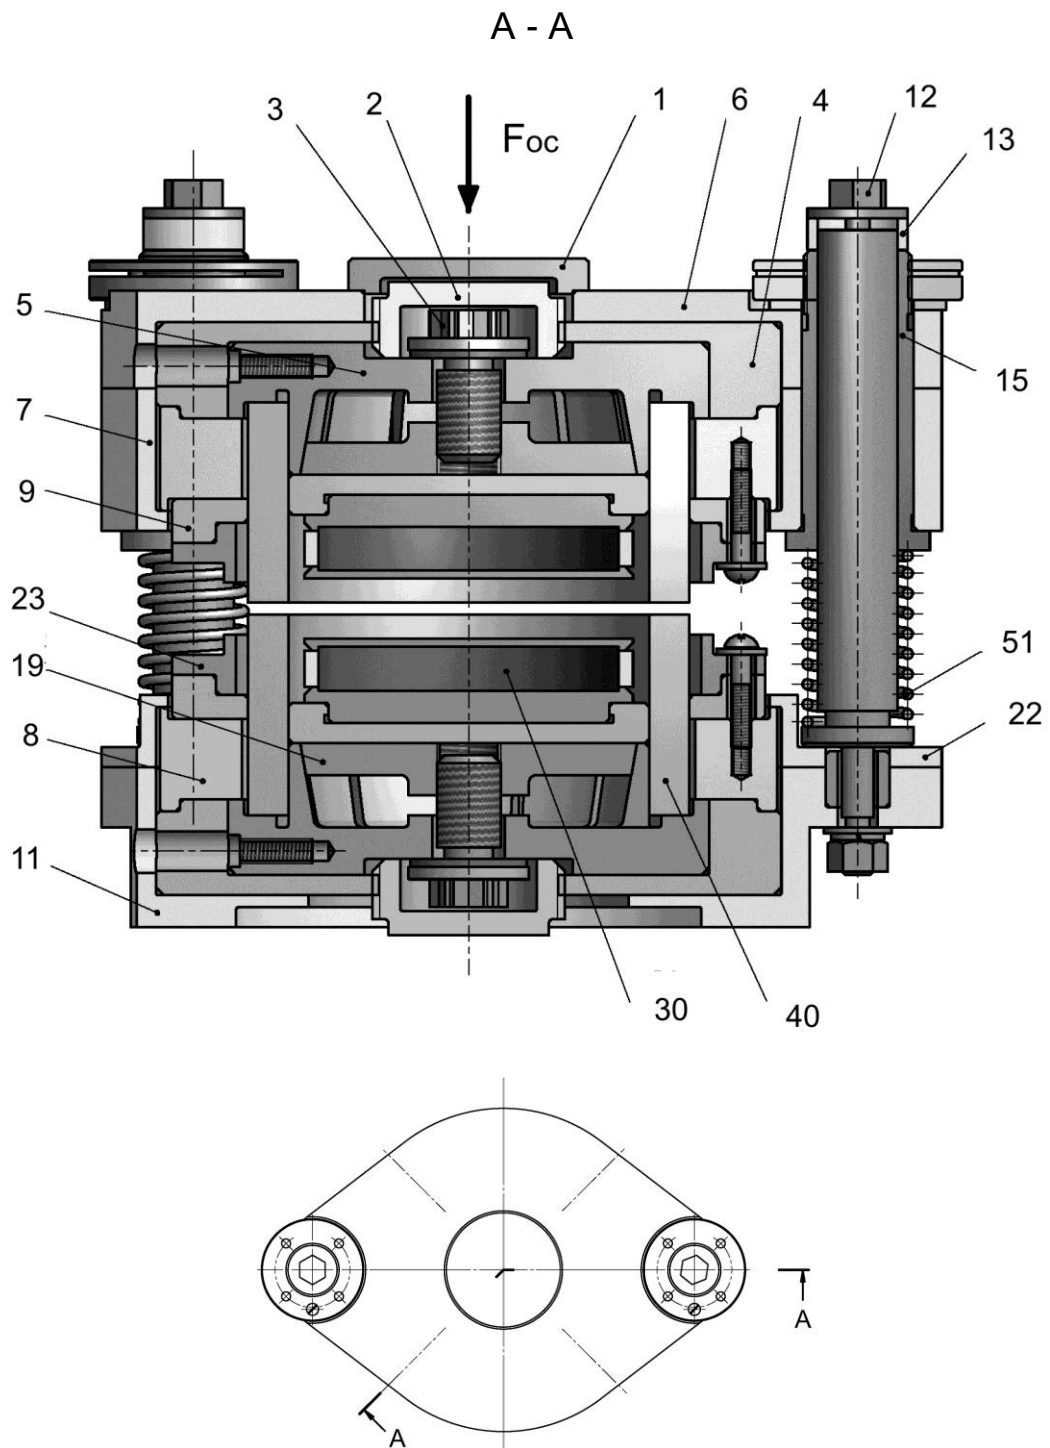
Установочное приспособление для сварки трубных заготовок переходников диаметром 110 мм
